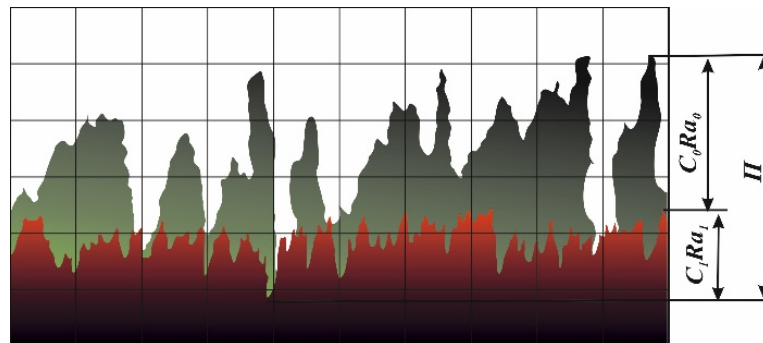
Схема шероховатости поверхности до и после шлифования тонкозернистым кругом
